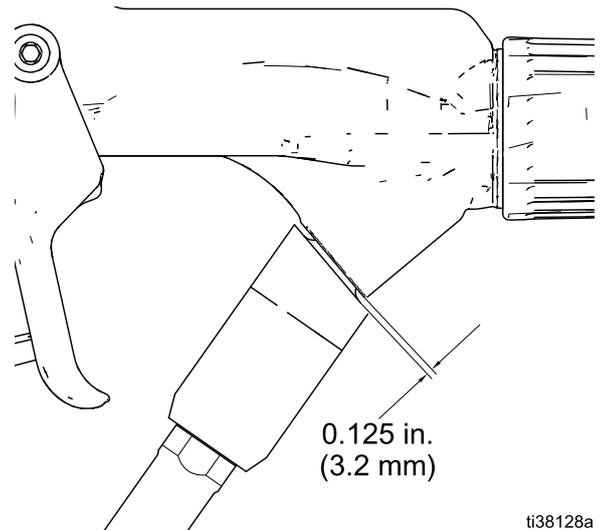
Ausrichtung von Verschraubung und Pistolenauslass
